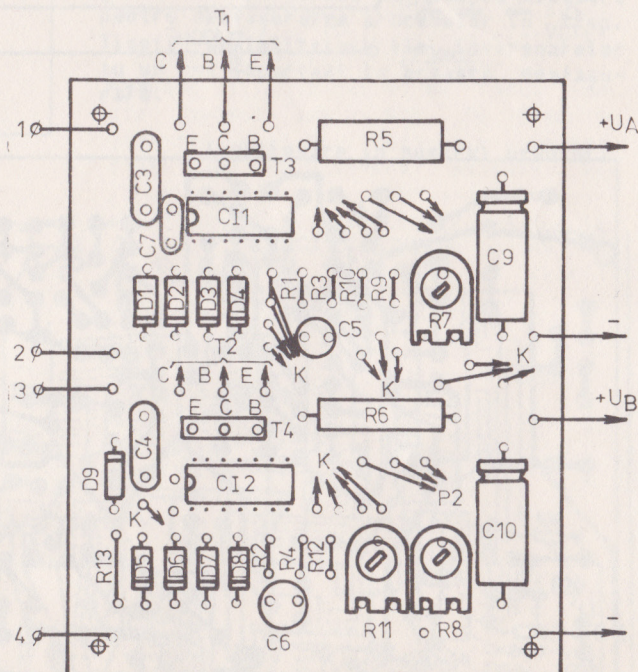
Amplasarea componentelor (vedere dinspre partea plantată)
